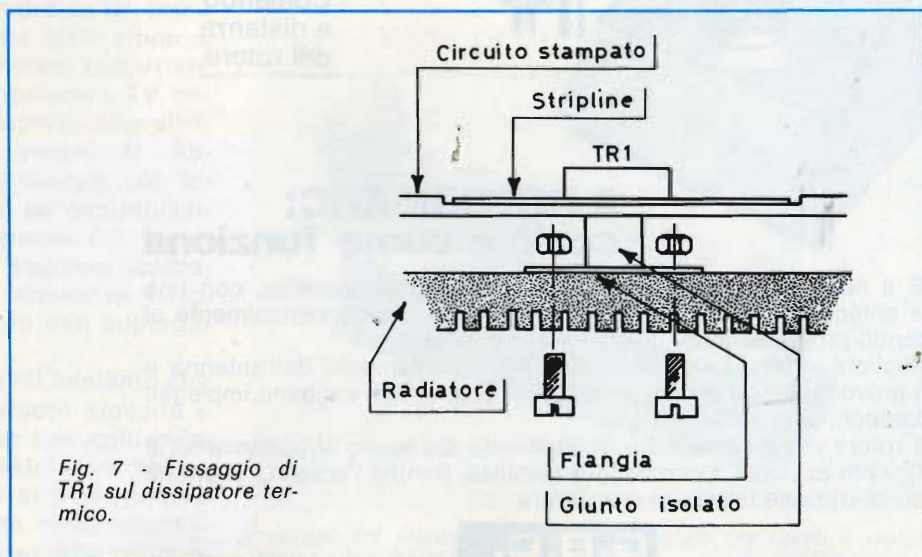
Fissaggio di TR1 sul dissipatore termico.
